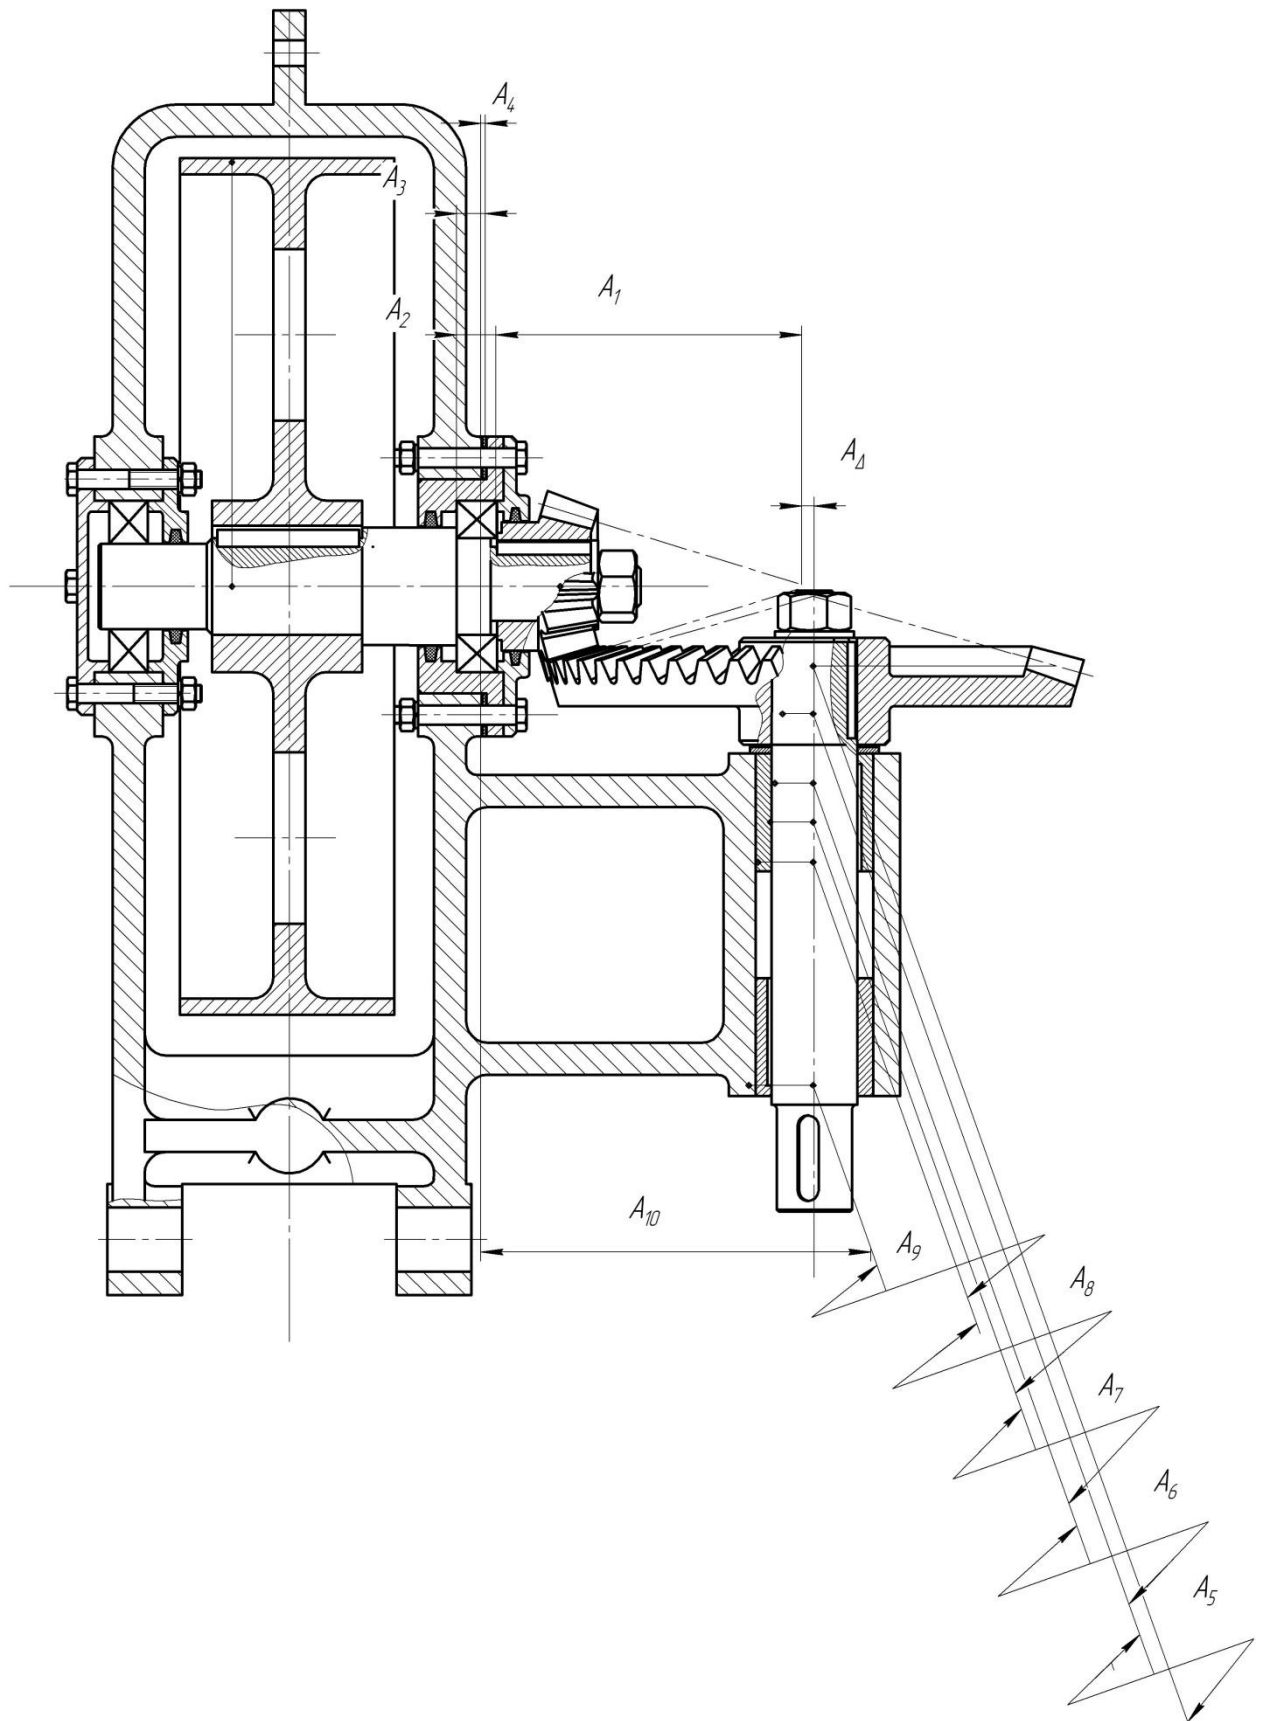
Розмірний ланцюг, який забезпечує точність розташування вершин ділільних конусів шестерні і зубчастого колеса в горизонтальній площині
